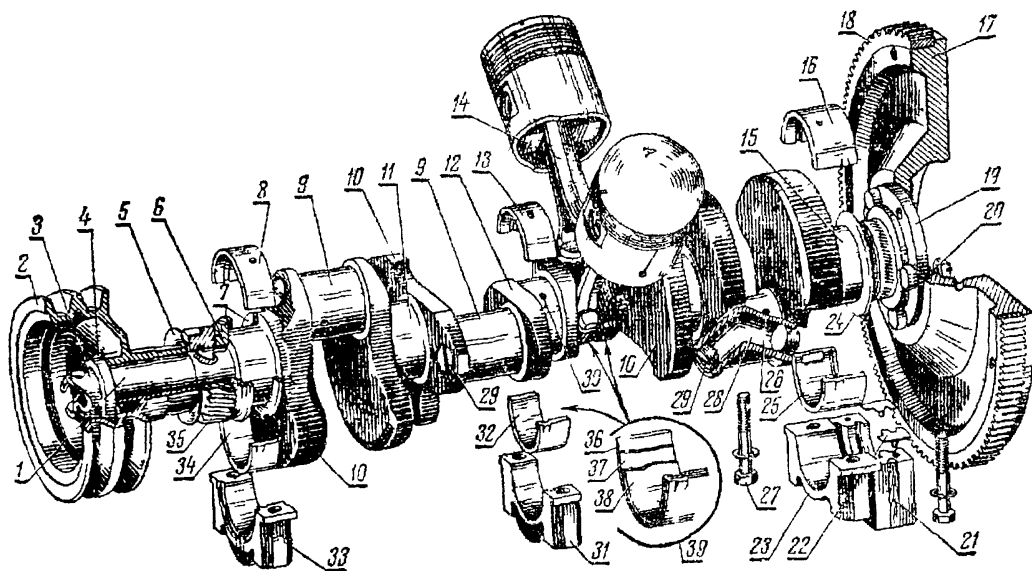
Кривошипно-шатунний механізму двигуна:
